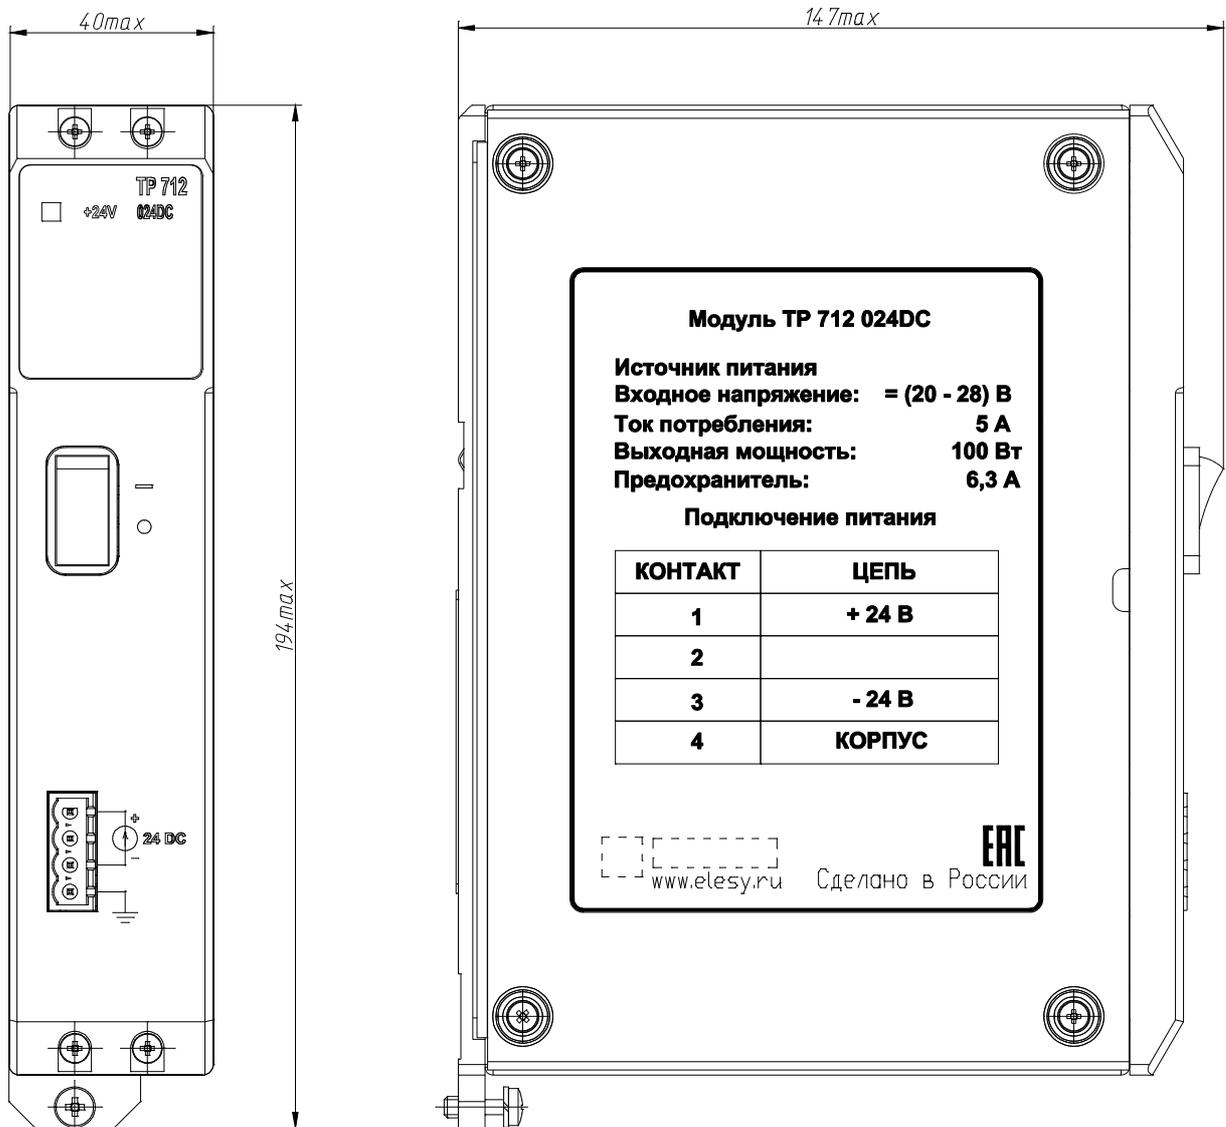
Внешний вид и габаритные размеры модуля
